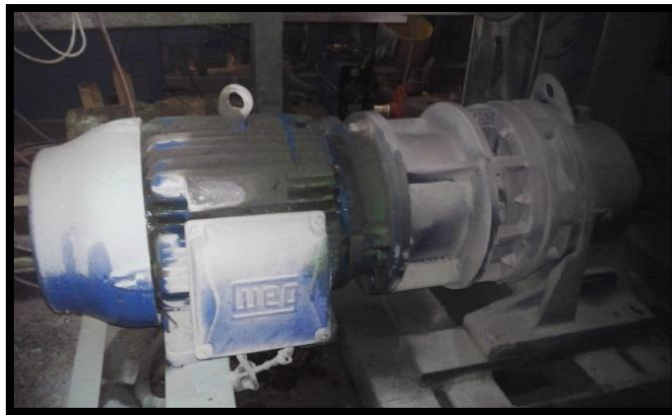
Motor principal de la extrusora línea 1 Empresa Tuboplex.
